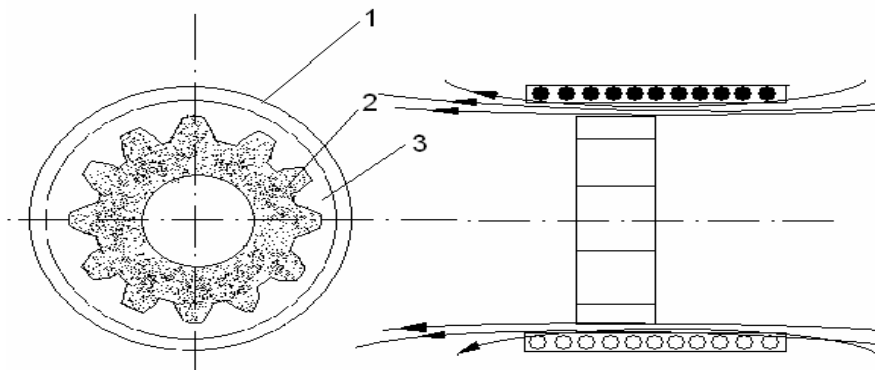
Схема индукционного нагрева зубчатого колеса под посадку: 1 – индуктор ; 2 – зубчатое колесо ; 3 – воздух
